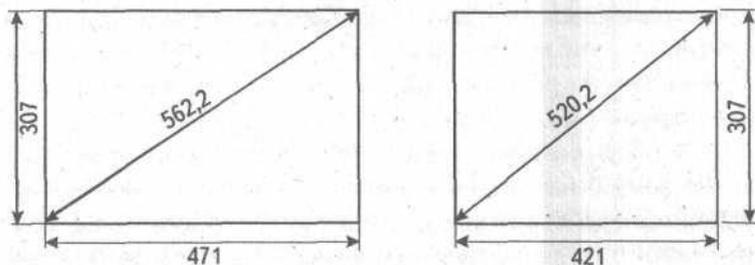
Шаблоны для стенок корпуса Дадана
